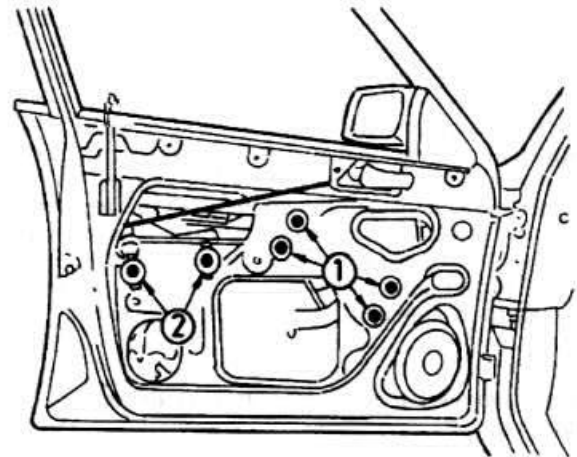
Заклепки (1) крепления стеклоподъемника передней двери и болты (2) крепления направляющей
